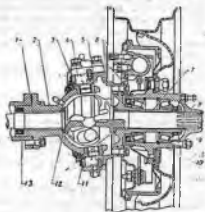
Поворотный кулак переднего ведущего моста. 1 — ведущий кулак, 2 — шаровая опора, 3 и 11 — регулировочные прокладки, 4 — шарикопев, 5 — корпус поворотного кулака, 6 — болт крепления шарфы поворотного кулака к корпусу, 7 — цапфа поворотного кулака, 8 — фланец ступицы, 9 — ведомый кулак, 10 — ступица, 12 — упорные шарфы шарира разных угловых скоростей, 13 — кожух полуоси.
